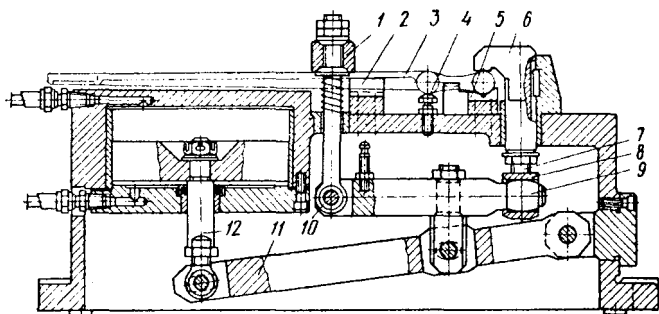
Двухместное приспособление для фрезерования торцов бобышек рычагов набором фрез
